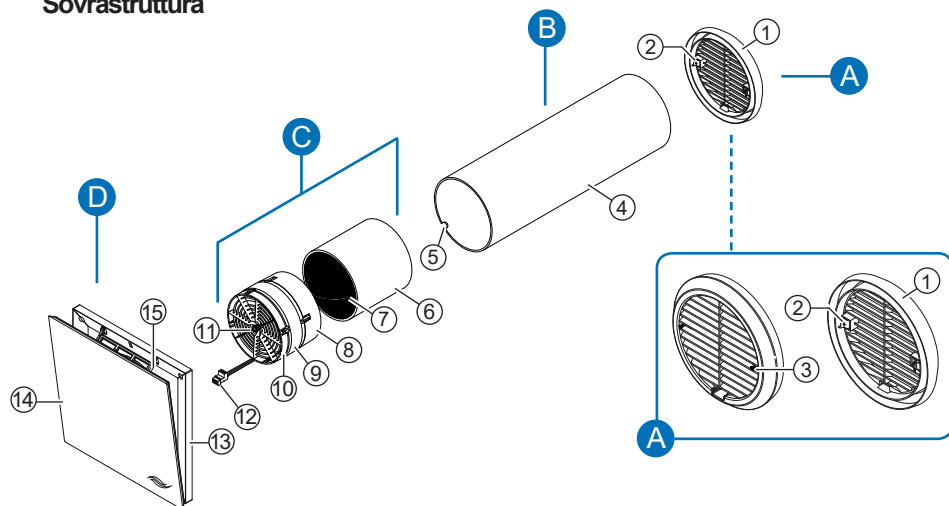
Panoramica dispositivo di ventilazione iV-Light
